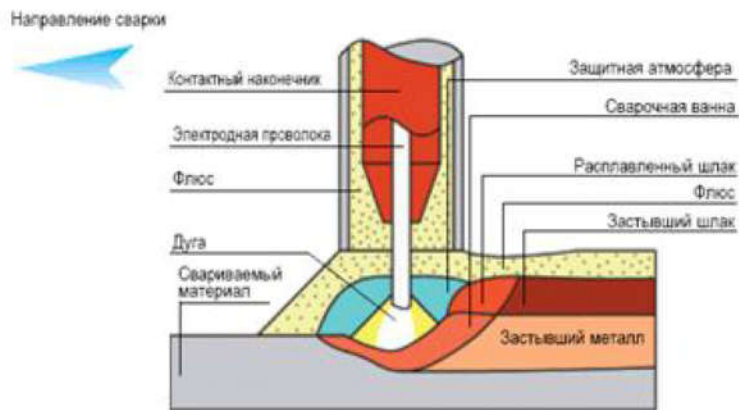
Схема сварки электрической дугой.
